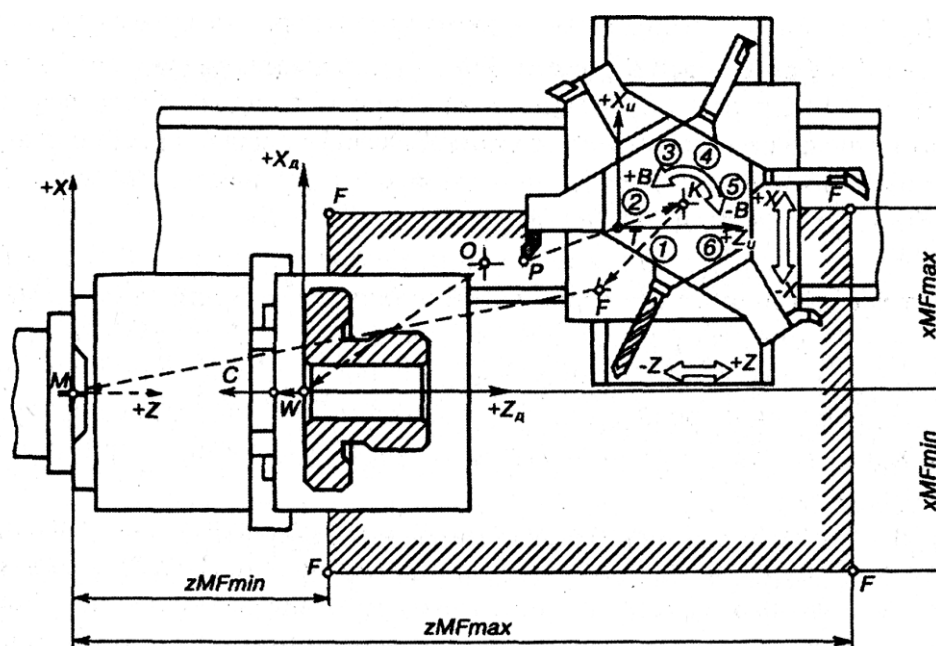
Связь систем координат программы, станка и инструмента при токарной обработке несколькими инструментами
